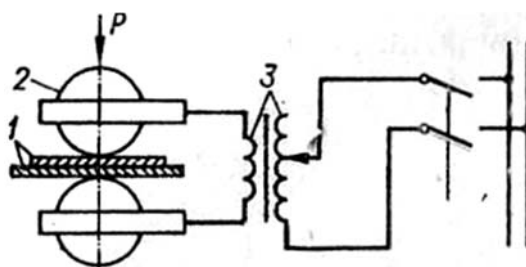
Схема роликовой сварки давлением
